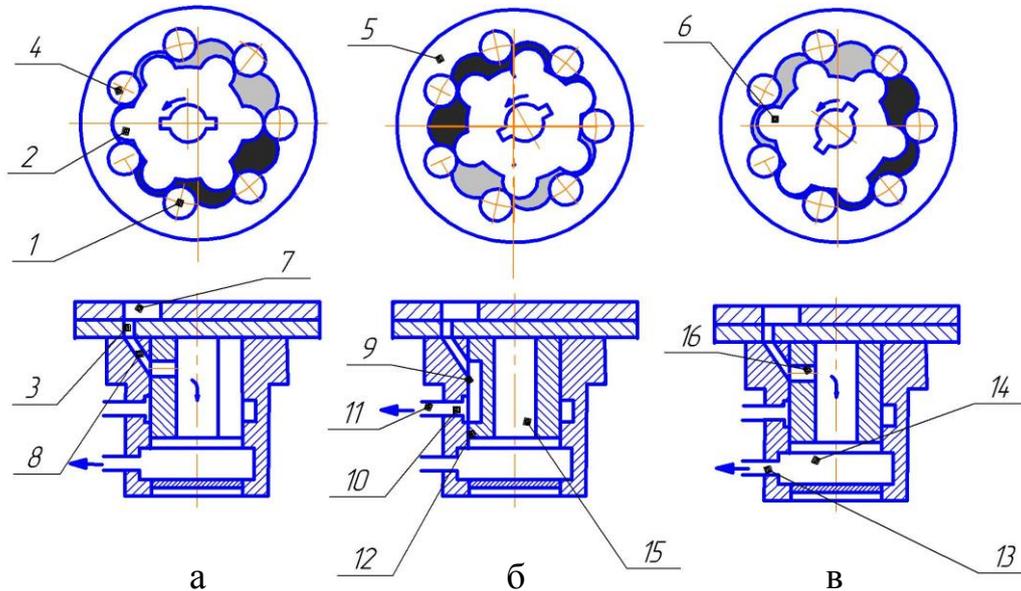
Схема работы насоса-дозатора: а, в – вытеснение рабочей жидкости; б – всасывание рабочей жидкости; 1, 4 – ролики; 2, 6 – зубья сателлита; 3 – отверстие; 5 – направляющая; 7 – рабочая камера; 8 – косой канал; 9 – паз; 10, 11, 13 – штуцера; 12 – золотник; 14 – кольцевые проточки; 15 – центральный осевой канал; 16 – радиальное отверстие.
